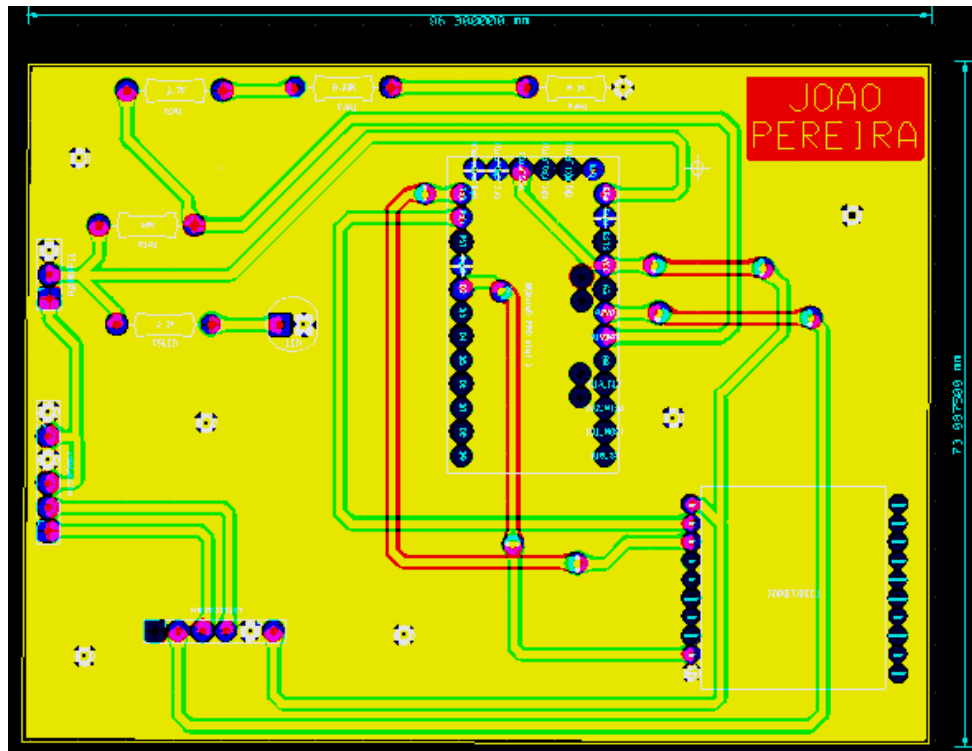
Design layout PCB placa mãe nó sensor local.
